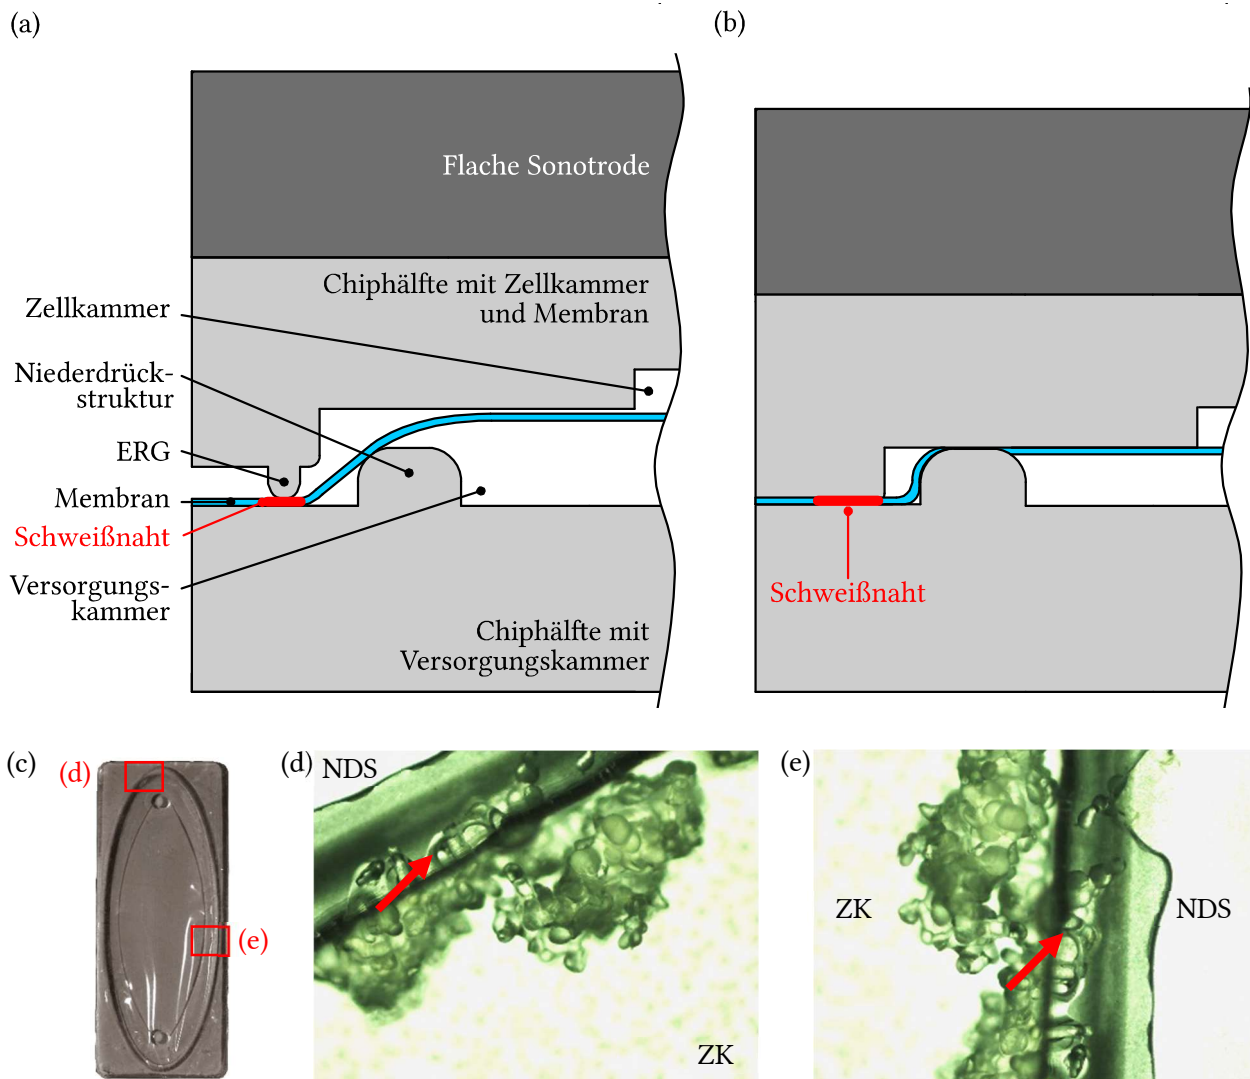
(a-b) Querschnitt des 200 µl-MBR vor dem Ultraschallschweißen, eine Niederdruckstruktur dient zum Spannen der Membran während dem Ultraschallschweißen, die entstehende Schweißnaht ist rot markiert, (c) Übersicht des 200 µl-MBR, (d-e) eingewachsene Pflanzenzellen im Restspalt zwischen den Chiphälften des 200 µl-MBR [126], rote Pfeile kennzeichnen eingewachsene Pflanzenzellen an verschiedenen Stellen des MBR zwischen Niederdruckstruktur (NDS) und Zellkammer (ZK), mit freundlicher Genehmigung von Phyton Biotech GmbH, © Phyton Biotech GmbH, 2016.
